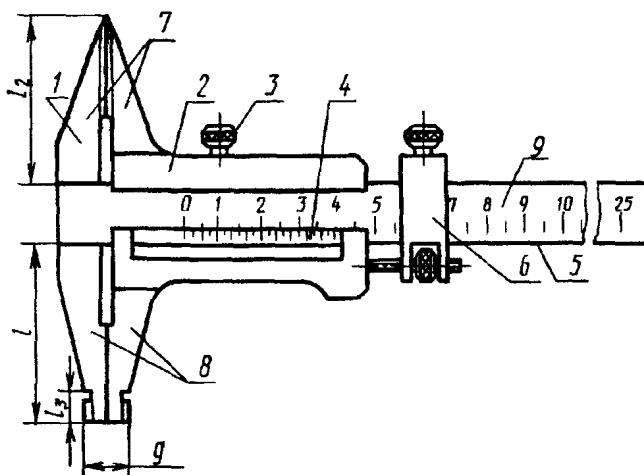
1- штанга; 2- рамка; 3- зажимаючий елемент; 4- ноніус; 5- робоча поверхня штанги; 6- пристрій точної установки рамки; 7- кромкові з вимірювальними поверхнями губки для вимірювання зовнішніх розмірів; 8- губки з плоскими та циліндричними вимірювальними поверхнями для вимірювання зовнішніх та внутрішніх розмірів; 9- шкала штанги
